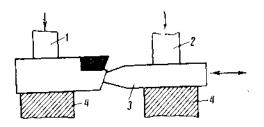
Схема нагрева для пайки твердосплавных резцов на стыковой сварочной машине:
